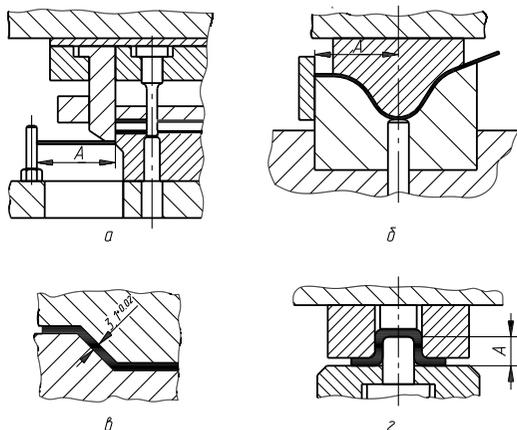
Примеры простановки спецразмеров, проверяемых при сборке штампов:
